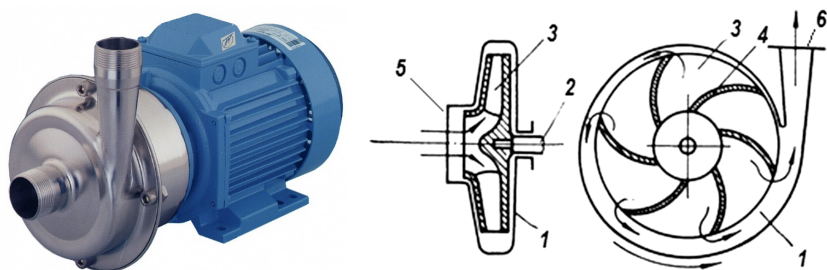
Общий вид и устройство центробежного насоса:
